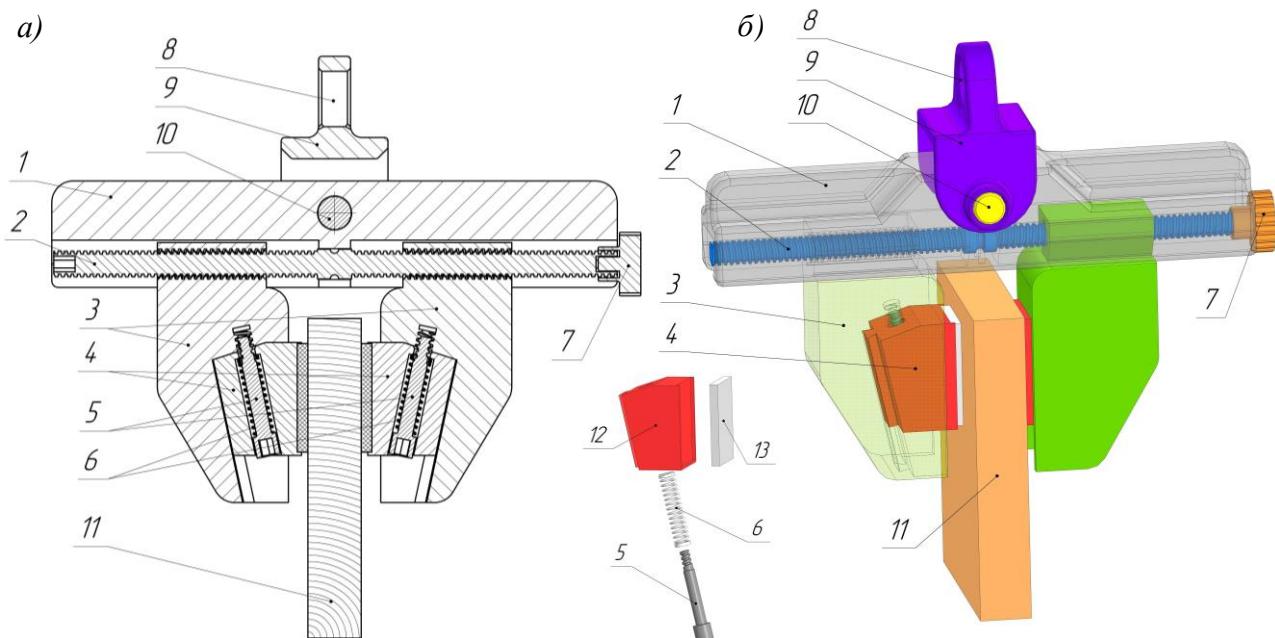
Фрикционно-зажимное ГЗУ с клиновыми упругоподатливыми КЭ для перемещения изделий из древесины толщиной до 200 мм: а – общий вид; б – 3D-модель; 1 – корпус; 2 – зажимной винт; 3 – ползун; 4 – клиновый контактный элемент; 5 – крепежный винт; 6 – возвратная пружина; 7 – маховик; 8 – скоба; 9 – скоба; 10 – ось; 11 – изделие из древесины; 12 – опорный корпус; 13 – накладка из упругоподатливого материала.
